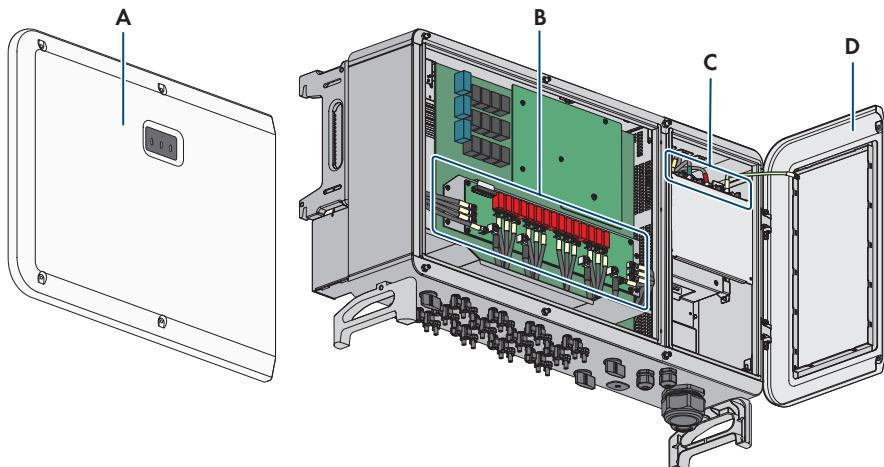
Positionen der Komponenten des Wechselrichters
